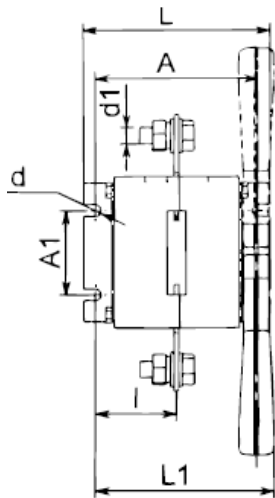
Выключатель-разъединитель однополюсный на одно направление с боковой рукояткой.
